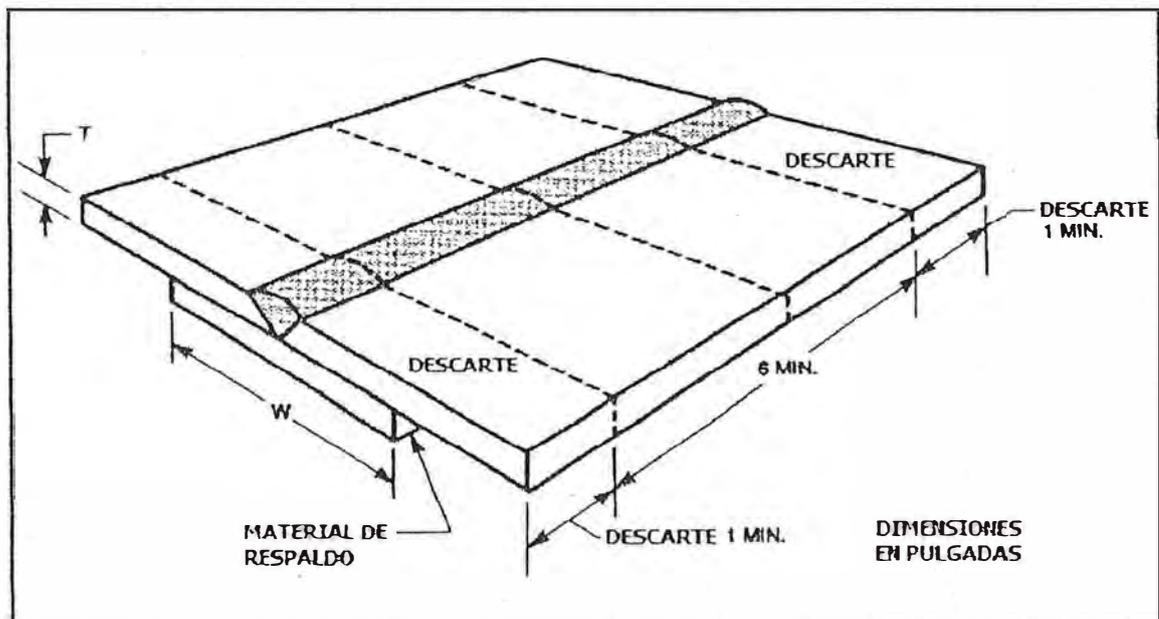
Localización de especímenes de doblado transversal – Plancha
